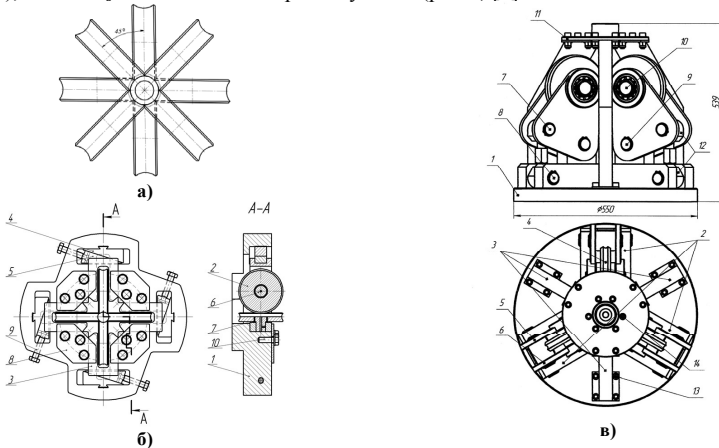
Схема обтискання трубчастої заготовки між роликами (а) і варіанти конструкції пристосування: чотири ролика (б), три ролика (в)
